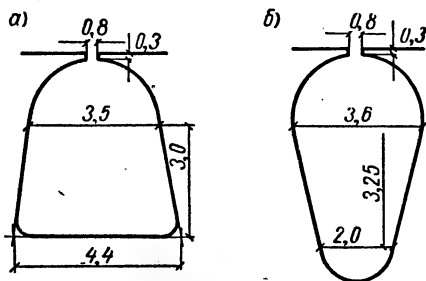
Эскизы пазов статора и ротора ВТ:
